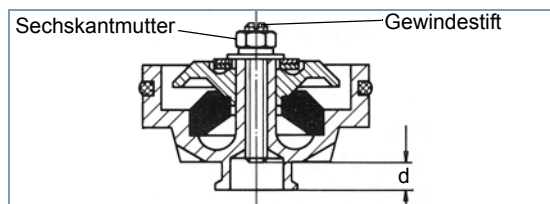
Maß d (Gerät mit einer Gummifeder)
